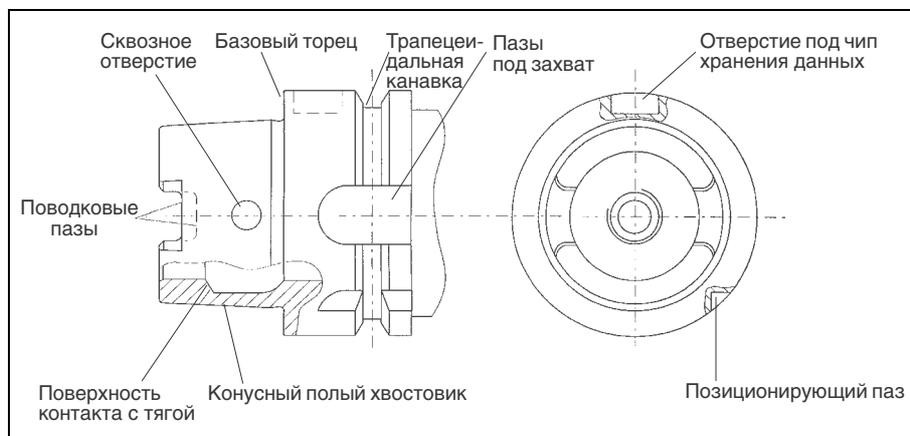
Конструктивные элементы HSK-конуса по стандарту DIN 69893, форма А
